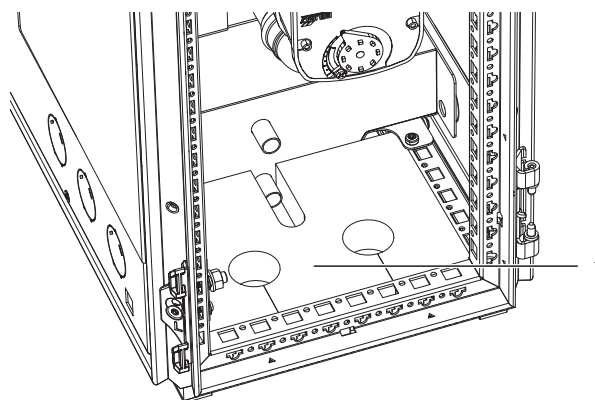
Vista posterior LCP CW – Espacio para introducir los tubos de conexión
